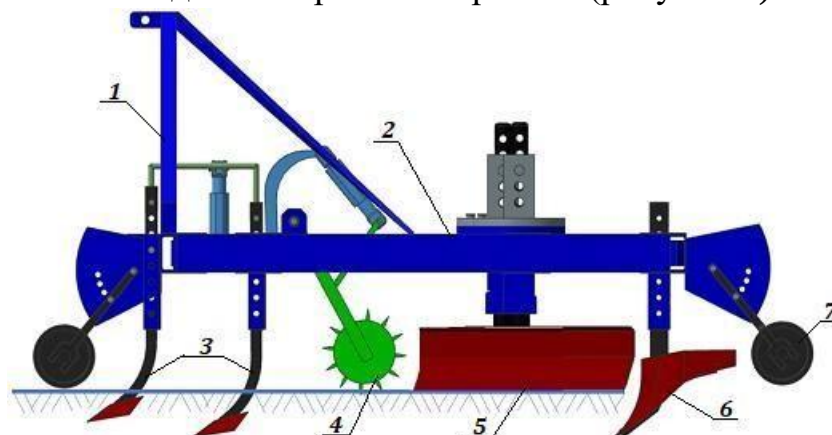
Схема расположения корпусов комбинированного агрегата:
